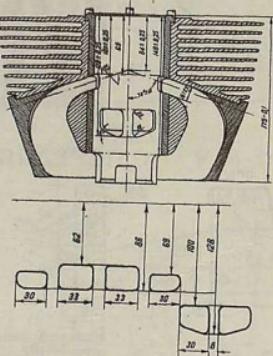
Цилиндр двигателя ИЖ-57 и его развертка (внизу).
